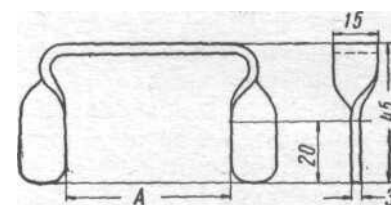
Скоба для закрепления поршней колесного тормозного цилиндра автомобиля модели 407
